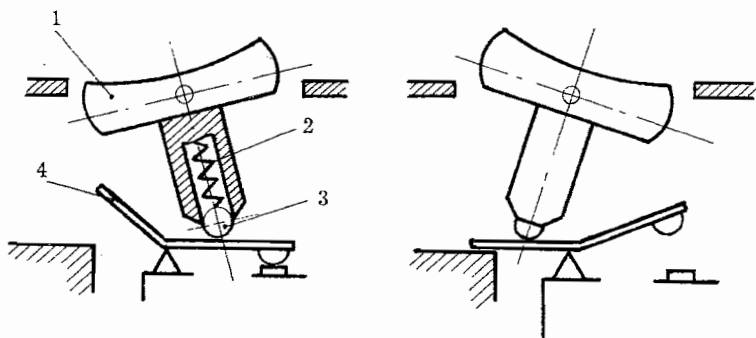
Конструкция качающего механизма выключателя с пружиной сжатия: 1 — клавиша; 2 — пружина; 3 — шарик; 4 — коромысло.
